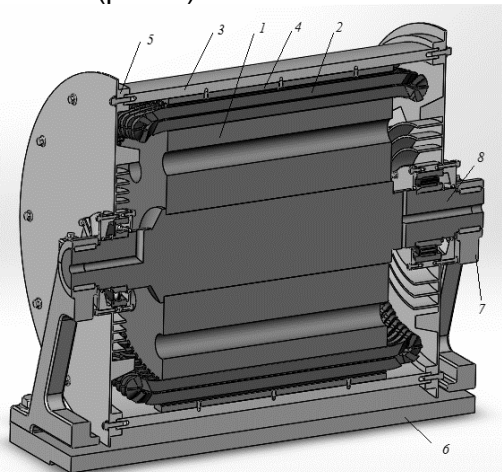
Разрез трехмерной модели обращенного СДПМ: 1 – статор; 2 – обмотка статора; 3 – ротор; 4 – магниты; 5 – подшипниковые щиты; 6 – плита станины; 7 – кронштейны станины; 8 – подвижный вал
